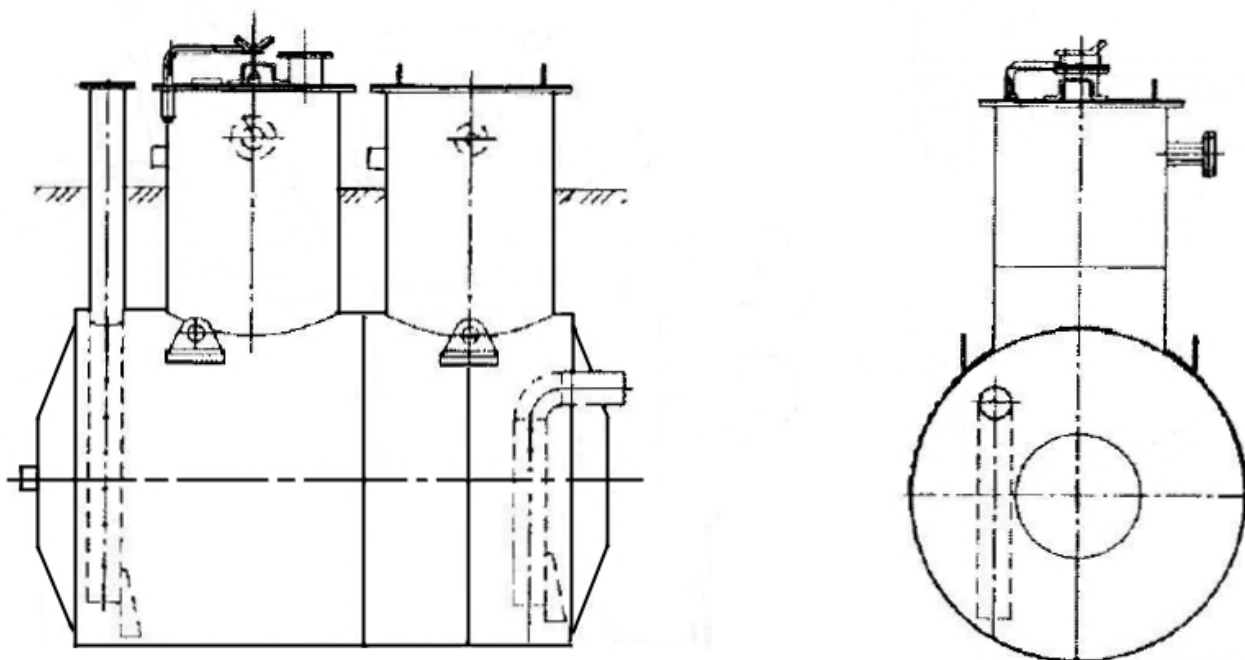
Общий вид резервуара ЕП-5-1600-600-А-С-У1
